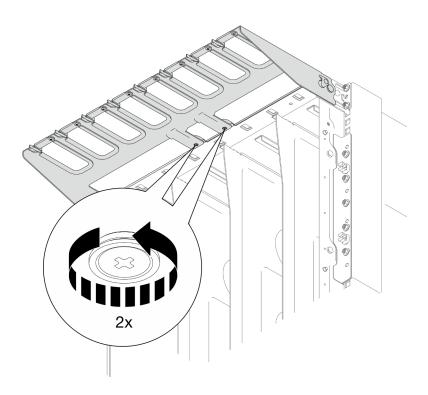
Extracción de dos tornillos desde debajo de la abrazadera de soporte frontal superior.
